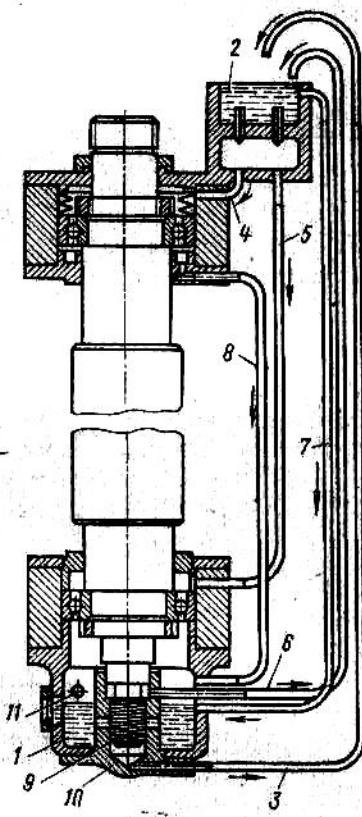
Непрерывная циркуляционная смазка шпинделя фрезерного станка (при 8000—10 000 мин⁻¹):
